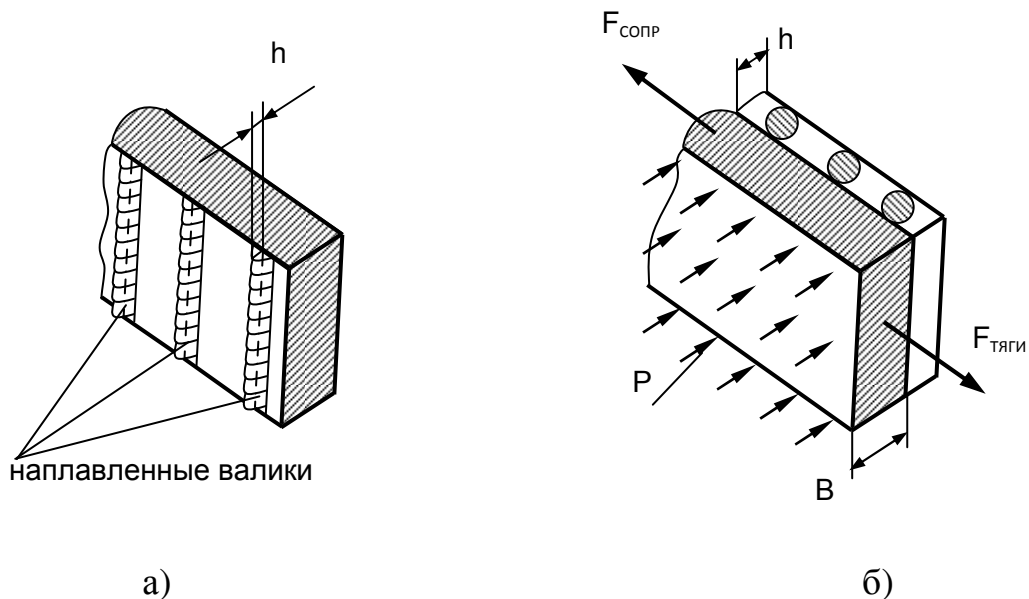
Поверхность лемеха: а – рабочая поверхность; б – вид с тыльной стороны;  $h$  – высота наплавленного валика
